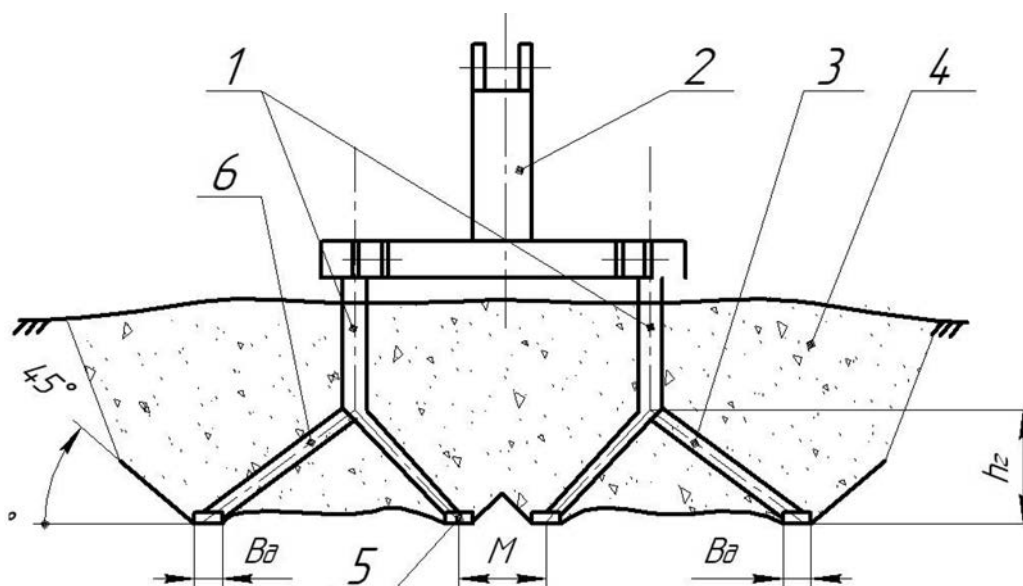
Схема расположения двухступенчатого двухрядного глубокорыхлителя (вид спереди):
